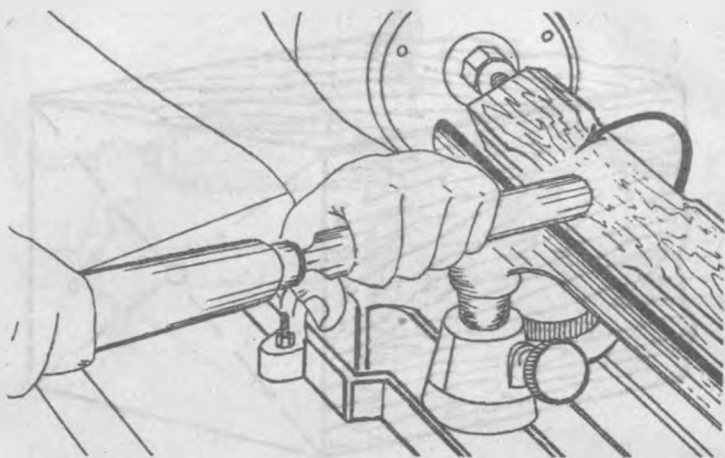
Предварительная грубая обработка заготовки при помощи рейера
